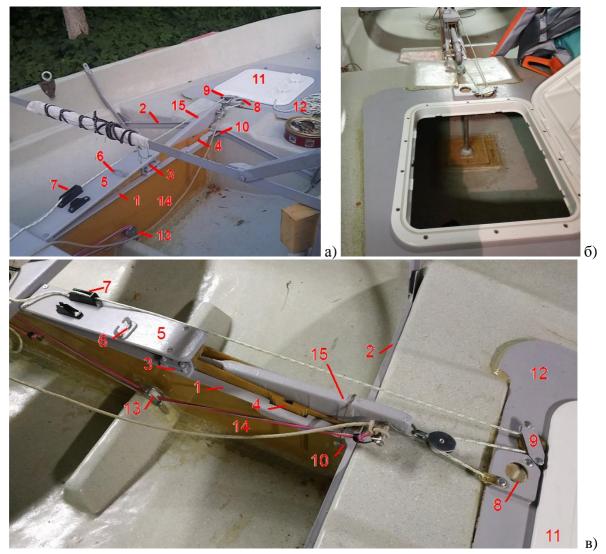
Усилитель швертового колодца и бортов: а) вид с кормы и левого борта; в) вид сверху и левого борта; б) пиллерс поддержки степса мачты распирает днище и полубимс под палубой (сосновый брусок 50 x 60 x 300).
